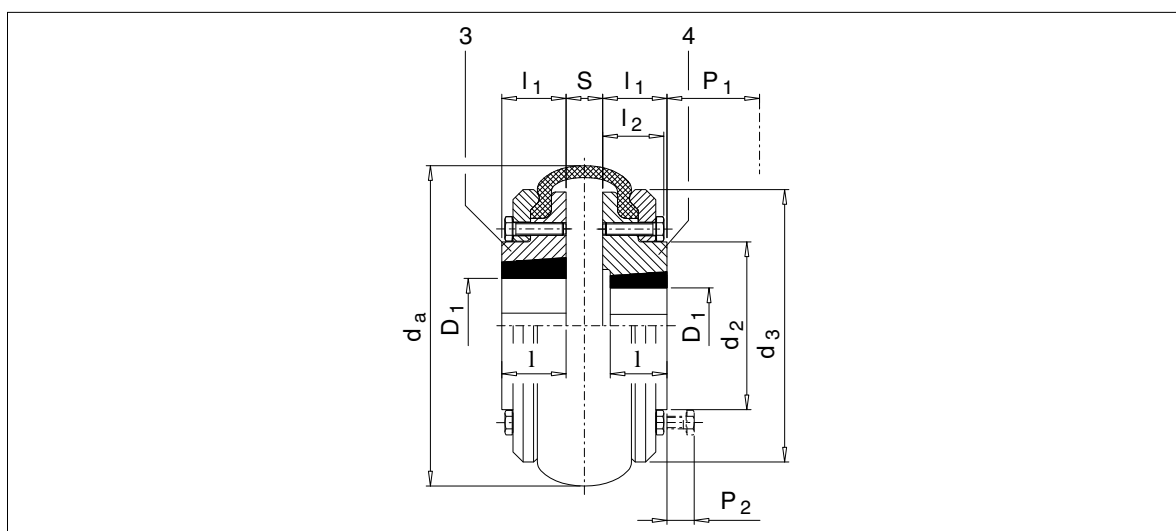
Чертеж с размерами типа EBWT, размеры 190 до 560
